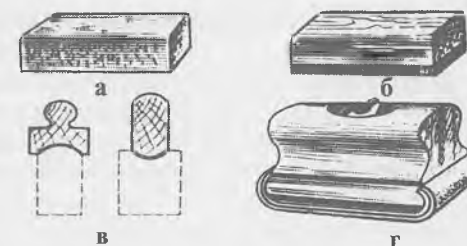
Колодки для шлифования: а — из пробкового дерева; б-в — из древесины с эластичной подошвой; г — с зажимом шлифовальной шкурки
